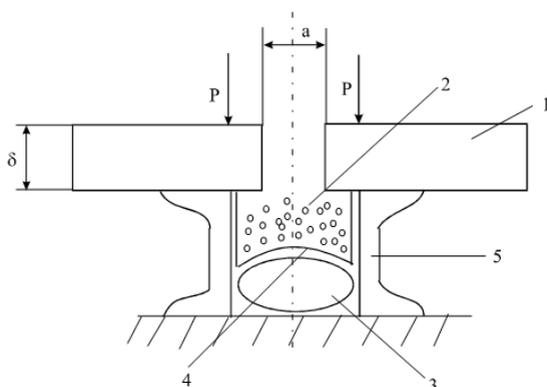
Схема сварки на флюсовой подушке: 1 – изделие; 2 – флюс; 3 – воздушный шланг; 4 – латунный лоток с флюсом; 5 – сварочный стол
